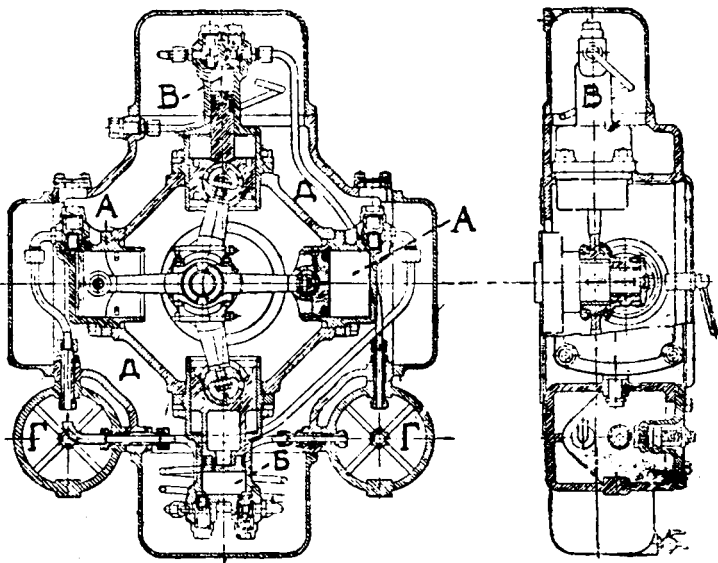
Компрессоръ трехступенчатый для двигателей высокаго сжатія (типа Дизель) для вбрызгиванія топлива и для пуска въ ходъ. Сист. Рива. а.—А, 2 цилиндра низкаго давления.—Б и В, средняго и высокаго давления.—Г, 2 цилиндрическія сборныя камеры, допускающія продувку излишней влаги.—Д, водяная рубашка, охлаждающая клапаны, цилиндры и штифты.
